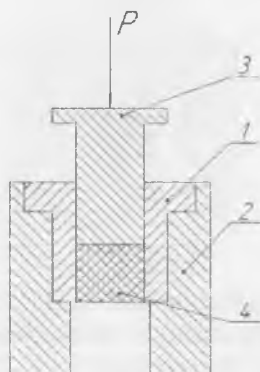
Схема проведения испытаний с использованием приспособления в сборе:
